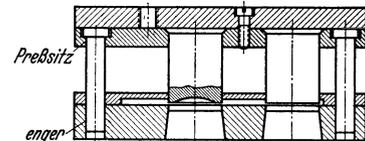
4-faches Schnittwerkzeug mit Bolzenführung.
